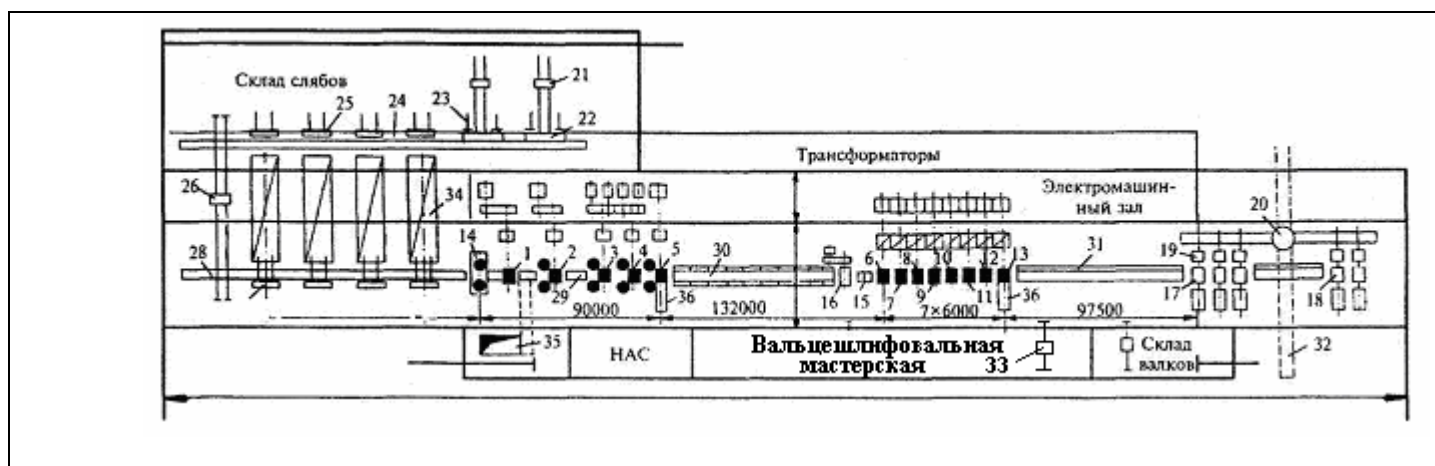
План расположения оборудования цеха горячей прокатки с непрерывным широкополосным станом 2000: рабочие черновые клетки: 1— 2-валковая; 2— универсальная 4-валковая; 3—5— непрерывная 3-клетевая группа универсальных 4-валковых клетей;
